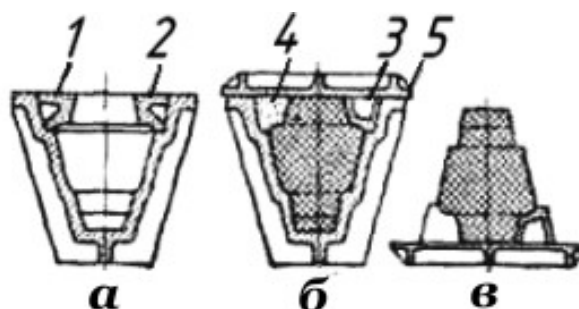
Изготовление стержней по ящикам с вкладышами: а – очистка, протирка, установка вкладышей 1, 2; б – набивка стержня, извлечение вкладышей, установка подставки 3 сушителя или заполнение этого промежутка отработанной формовочной смесью 4, накладывание на ящик сушильной плиты (драйера) 5, поворот ящика на 180°; в – снятие ящик со стержня, отделка и отправка стержня в сушило
